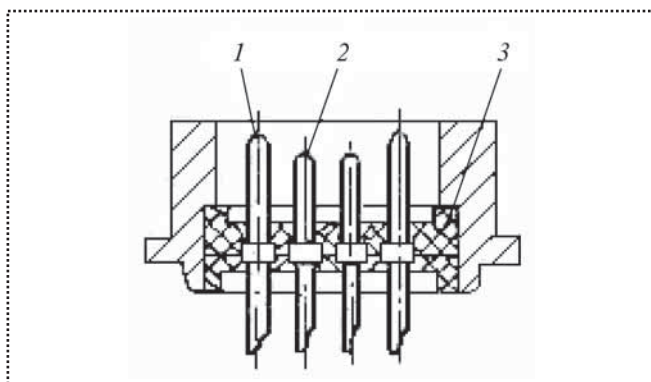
Контактный пакет комбинированного электросоединителя с цилиндрическими контактными элементами двух типов: 1, 2 – контактные элементы различного диаметра; 3 – основной изолятор
